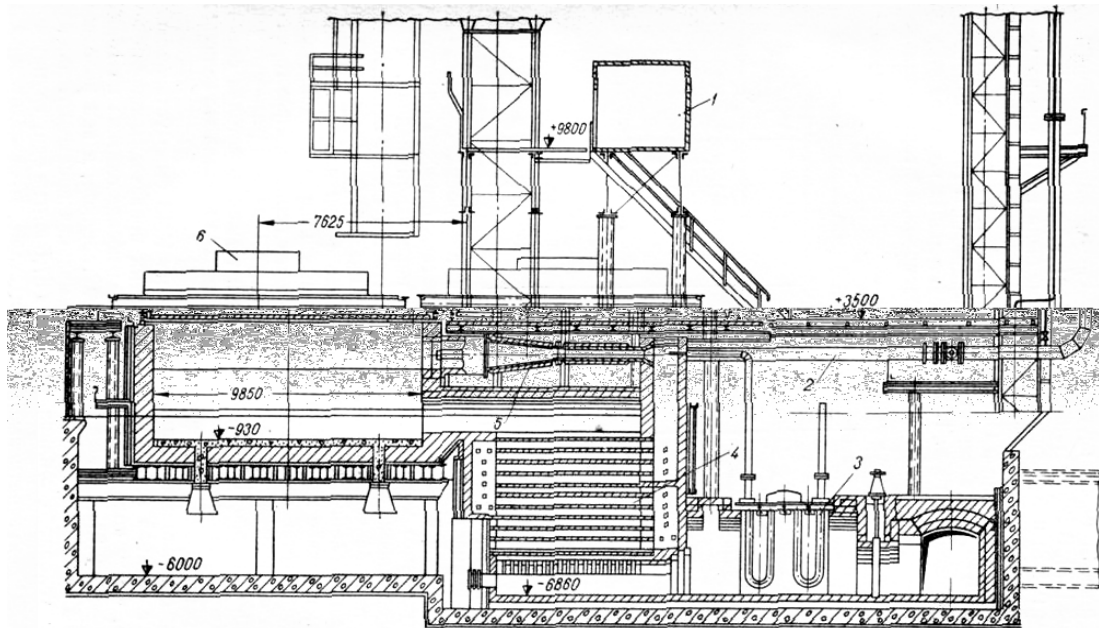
Общий вид и расположение элементов recuperативного нагревательного колодца с одной верхней горелкой: 1-помещение щита КИП; 2-газопровод; 3-металлический петлевой recuperатор для нагрева инжектирующего воздуха; 4-керамический recuperатор для подогрева воздуха; 5-инжектор; 6-напольный крышечный кран
